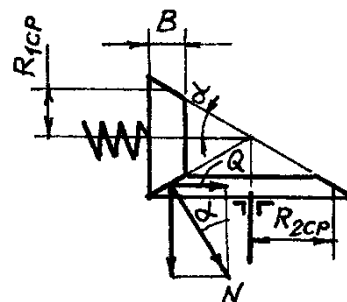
Розрахункова схема конічної фрикційної передачі / Fig. 2. Calculation scheme of conical friction gear
